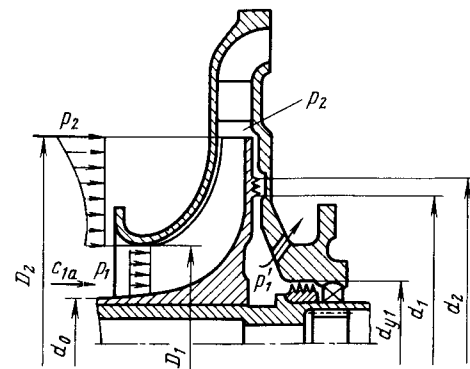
К расчету осевых сил колеса центробежного компрессора
